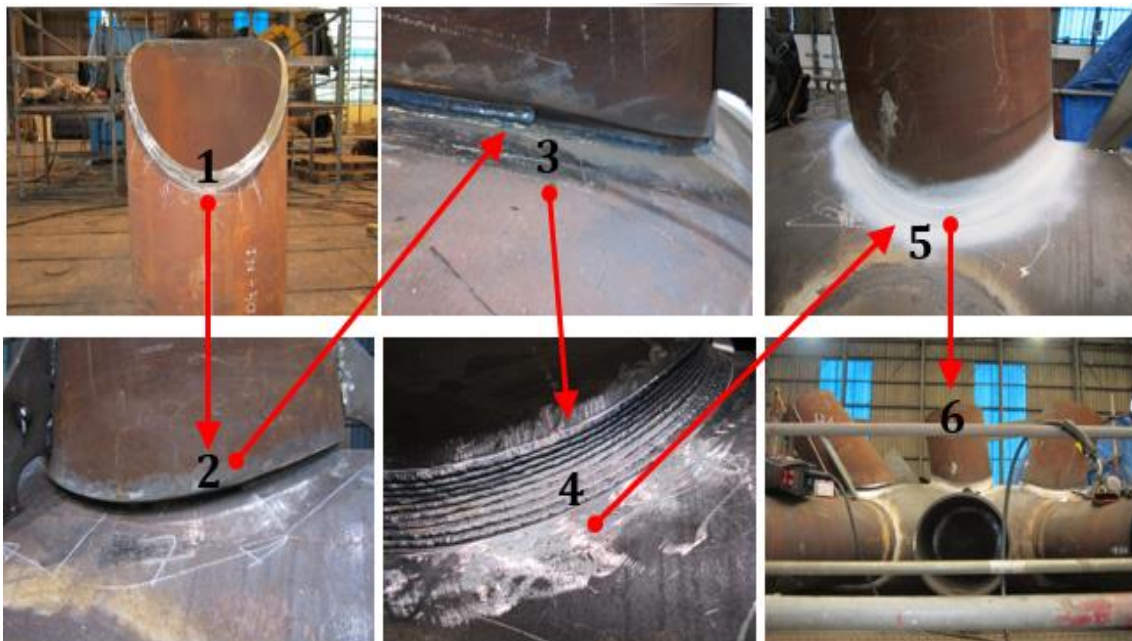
Realización de la soldadura de injertos en taller (Fuente: FEVE)
